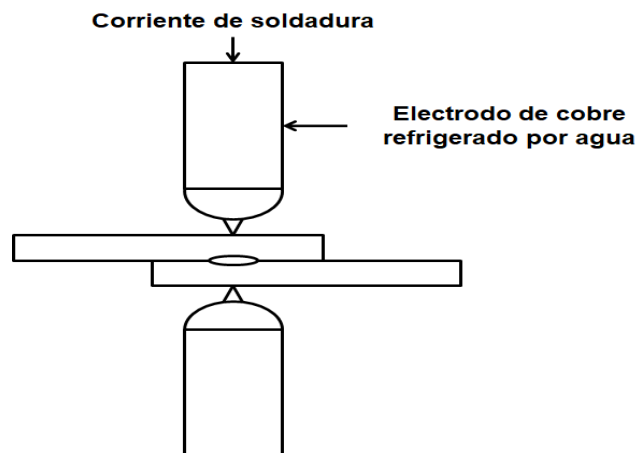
1 Representación de la soldadura de resistencia por puntos [32].
